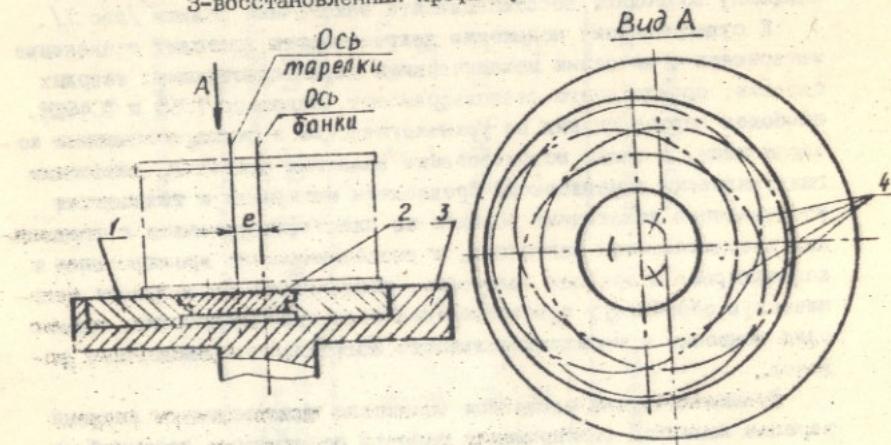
Эксцентричная установка опорной тарелки на подъемном столике. 1-опорная тарелка; 2-прижимной диск; 3-подъемный столик; 4-точка контакта с банкой.
